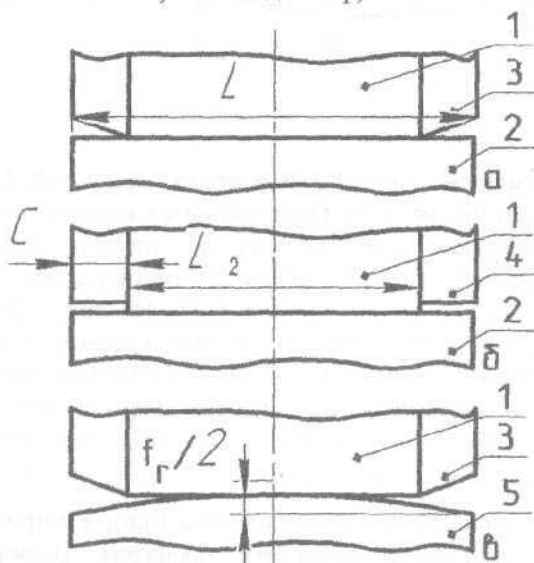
Типи початкових профілів валків (а – в): 1 – бочка опорного валка; 2 – робочий валок з циліндричним профілем створюючої; 3 – краєвий скіс опорного валка; 4 – краєвий врез опорного валка; 5 – робочий валок з опуклим профілем створюючої бочки
